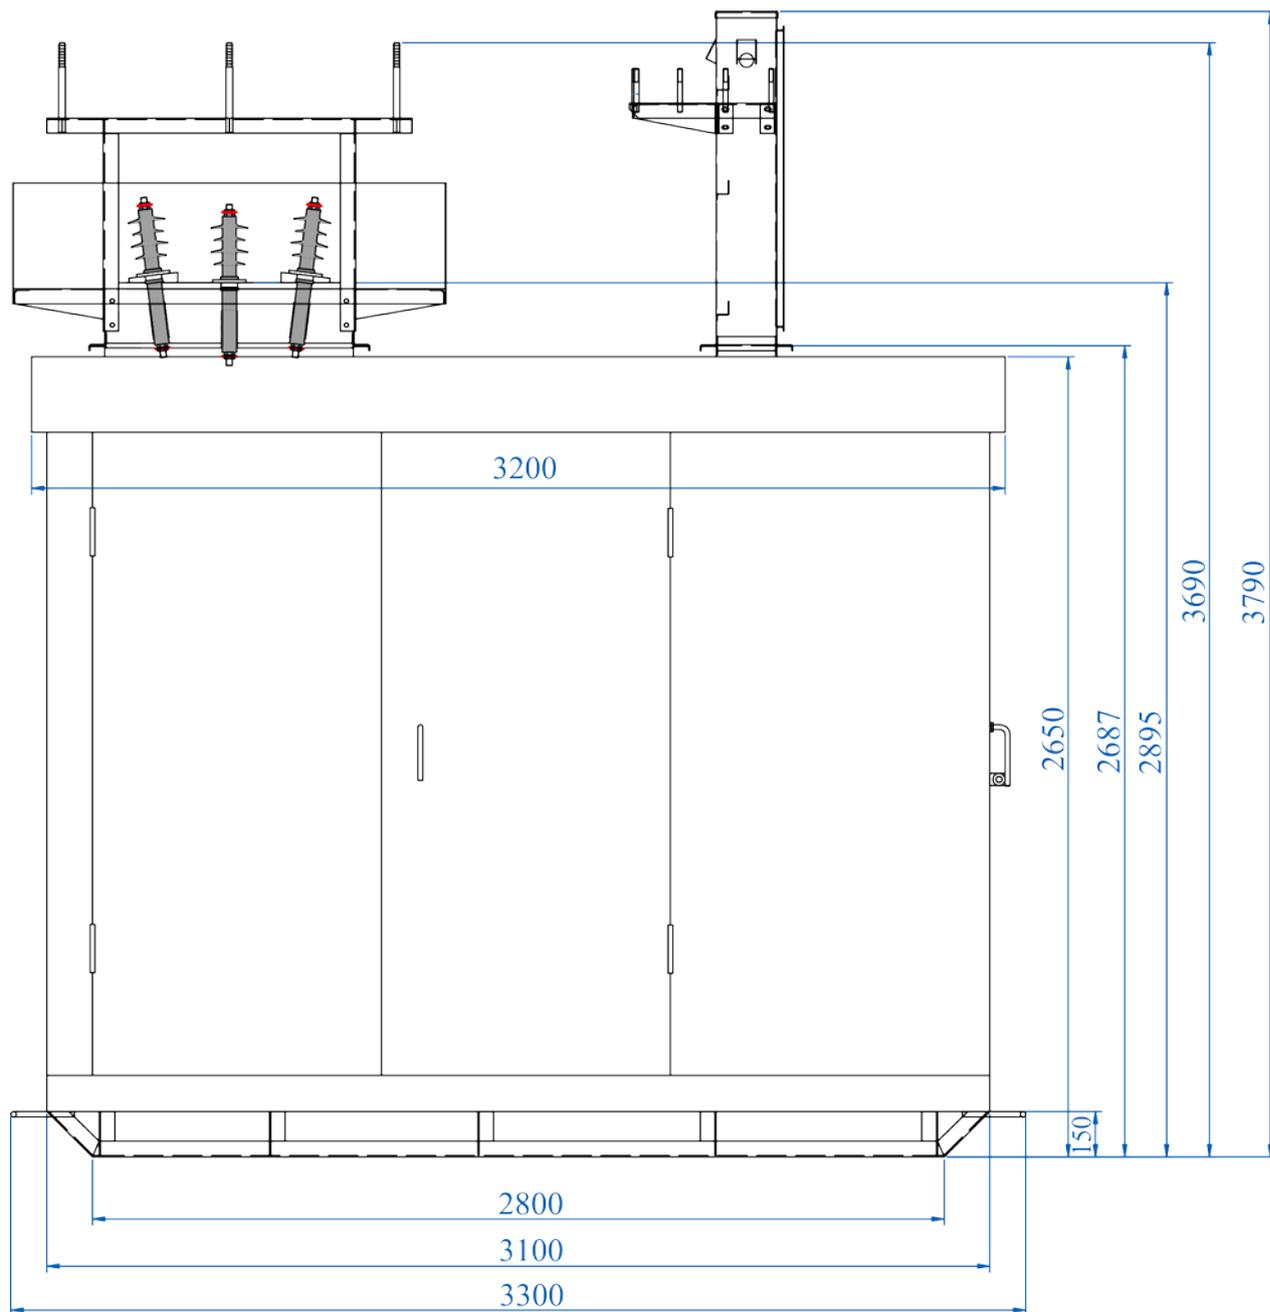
Внешний вид и габаритные размеры КТПН – 250, 400, 630 кВА
